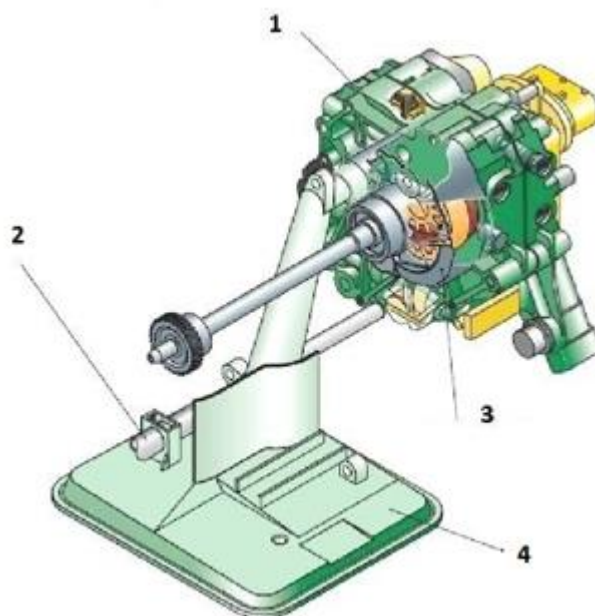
Гидравлический механизм вариатора: 1 – масляный насос; 2 – патрубок; 3 – привод насоса; 4 – резервуар для слива масла
